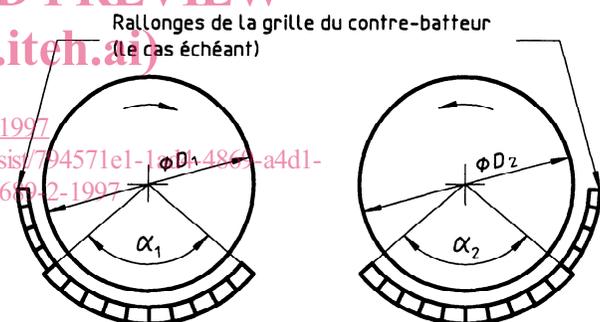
Cylindres ou rotors disposés longitudinalement (vue de l'arrière)
